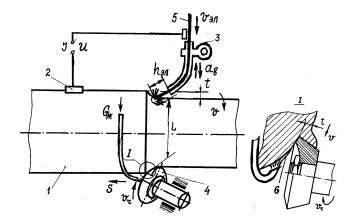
Наплавка проволокой с упрочняющим ротационным резанием:  $1-обрабатываемая деталь; 2-скользящий контакт; 3-мундштук наплавочной головки; 4-ротационный резец; 5-наплавочная проволока; 6-охлаждающая жидкость; V-скорость главного движения; <math>V_r$ -скорость дополнительного движения резца; S-скорость подачи;  $V_{\text{эл}}$ -скорость подачи электродной проволоки;  $h_{\text{эл}}$ -вылет электрода;  $G_{\text{ж}}$ -расход жидкости; I-сила тока; U-напряжение дуги; t-глубина резания; L-расстояние от электрода до резца
